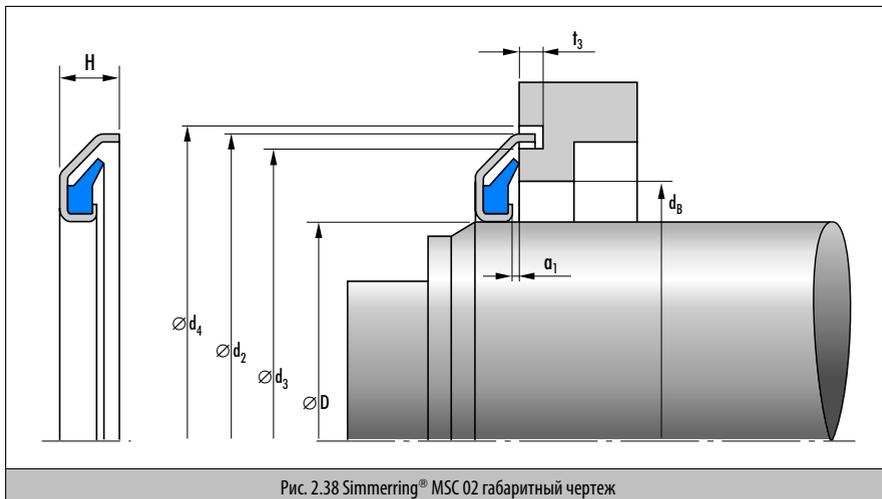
Simmerring® MSC 02 габаритный чертеж
